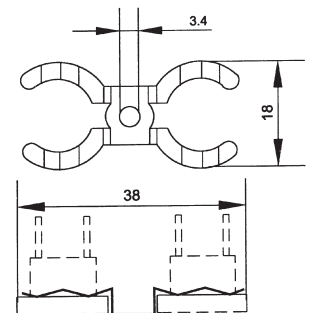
Zwillingsflansch spez. für 2 Thermostate
